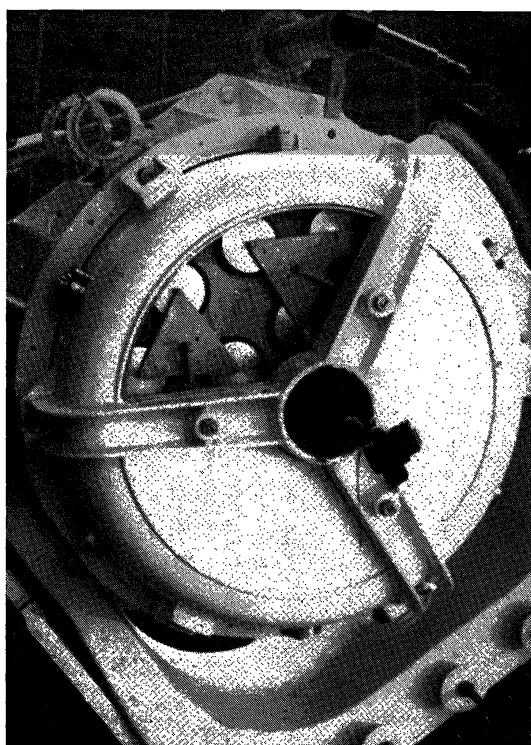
Le « coussin mécanique » vu par en dessous.
